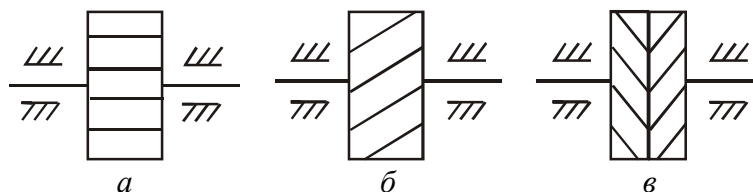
а – прямозубое зубчатое колесо; б – косозубое зубчатое колесо; в – шевронное зубчатое колесо
